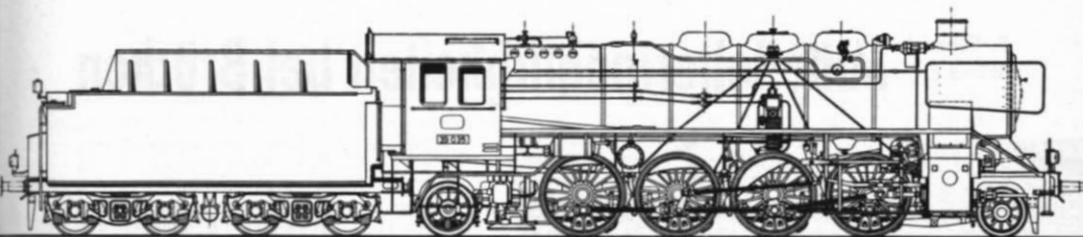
und 24. Seitenansicht und Draufsicht der BR 39 035 im N-Maßstab 1 : 160. Die Hauptmaße möge man den H0-Zeichnungen Abb. 1, 6 und 7 (hinter dem Schrägstrich) entnehmen.
